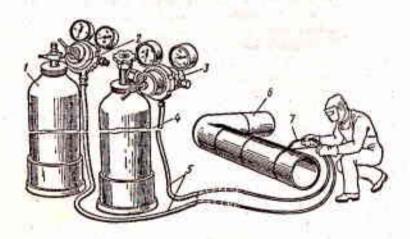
Оборудование для газовой сварки: 1, 4— баллоны, 2, 3— редукторы, 5— шланги; 6— труба; 7— горелка
